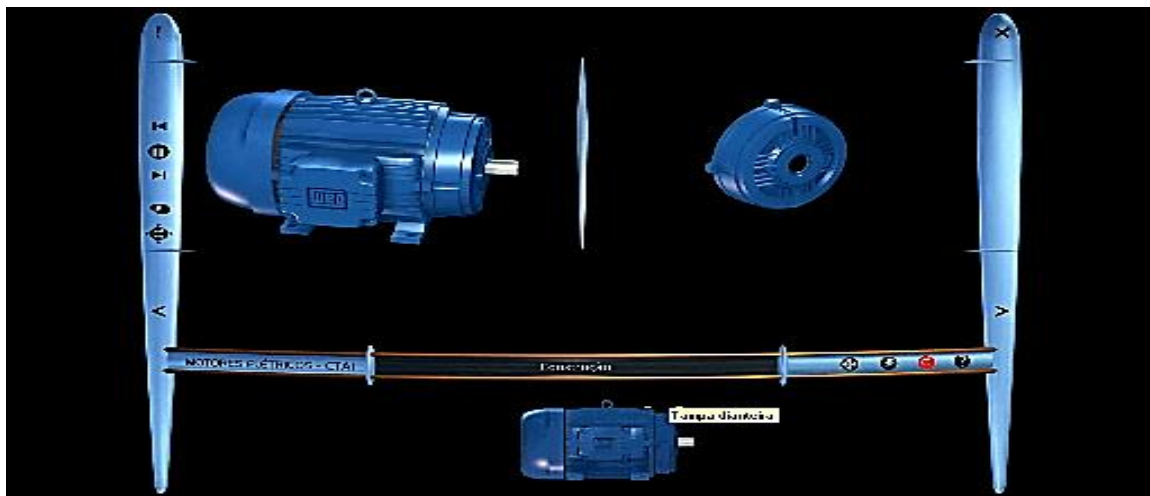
Partes de un motor trifásico (tapa delantera).
